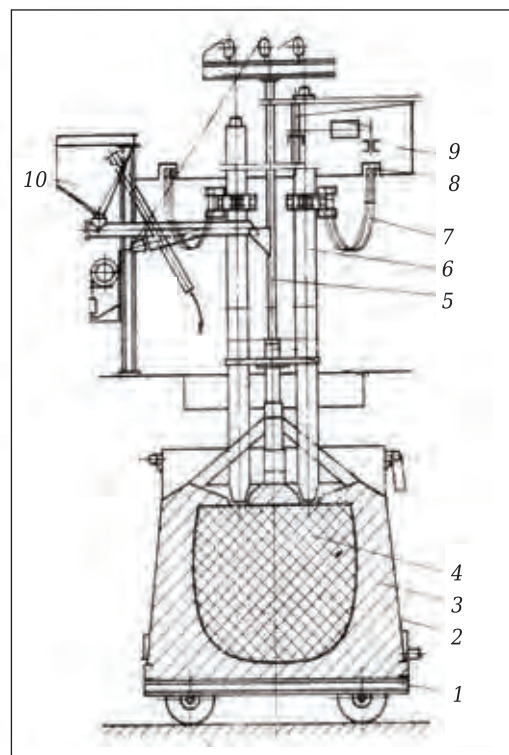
Электродуговая печь для плавки «на блок»: 1 — тележка; 2 — кожух; 3 — изоляция; 4 — плавленый материал; 5 — труба для загрузки шихты; 6 — электроды; 7 — короткая сеть; 8 — подвод тока; 9 — кожух для удаления газов; 10 — бункер с шихтой
